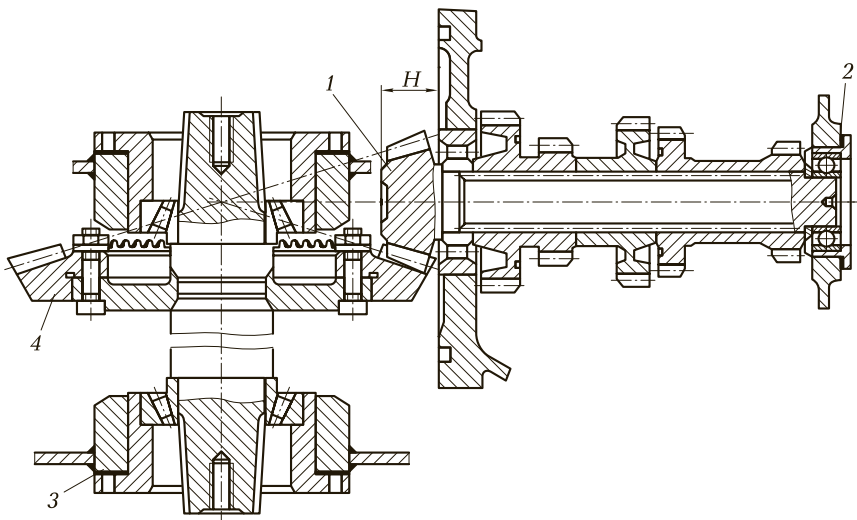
Регулирование бокового зазора в конической зубчатой передаче:
